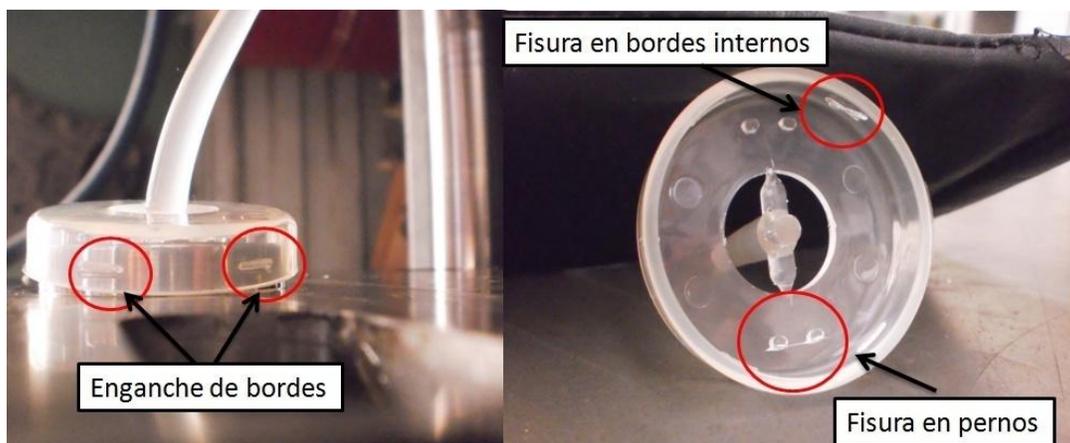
Enganche de la pieza actuador en el inserto por parte de los bordes internos (izquierda). Fisura sobre los pernos y bordes internos de la pieza actuador (derecha).
